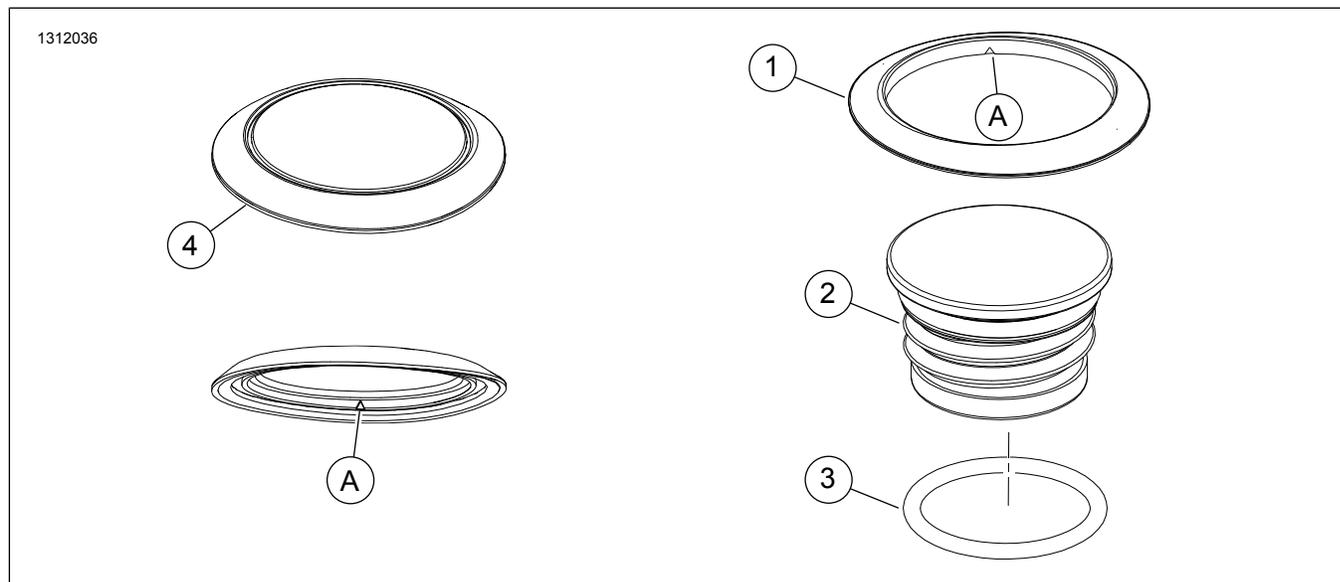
Pièces de rechange : Kit de bouchon de carburant encastré
